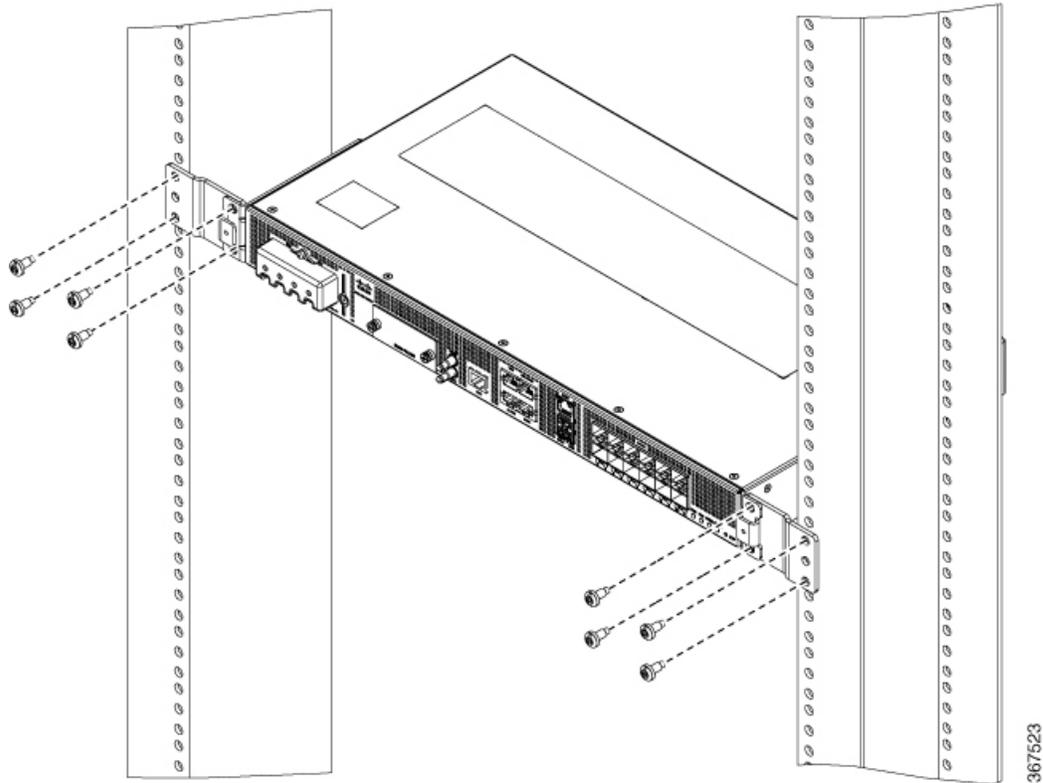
Installer l'appareil sur un rack de 23 pouces (montage avant)
